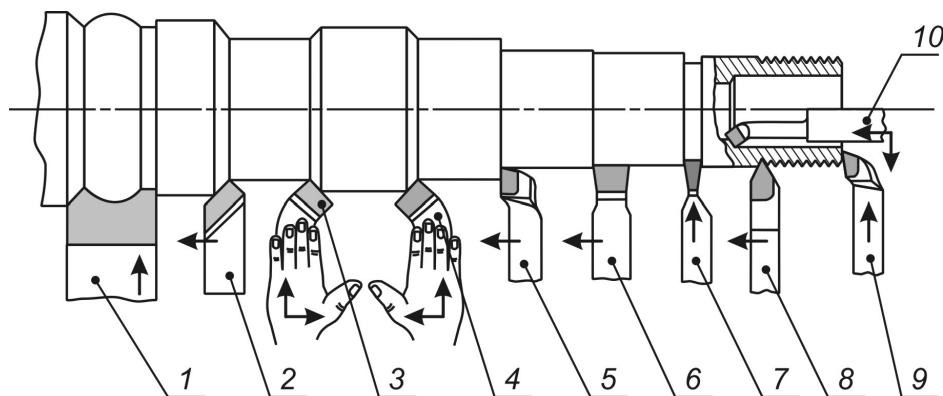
Основные типы токарных резцов: 1 - фасонный, 2 - проходной прямой, 3, 4 - проходной отогнутый, 5 - проходной упорный, 6 - для чистовой обработки, 7 - отрезной, 8 - резьбовой, 9 - подрезной, 10 - расточные
